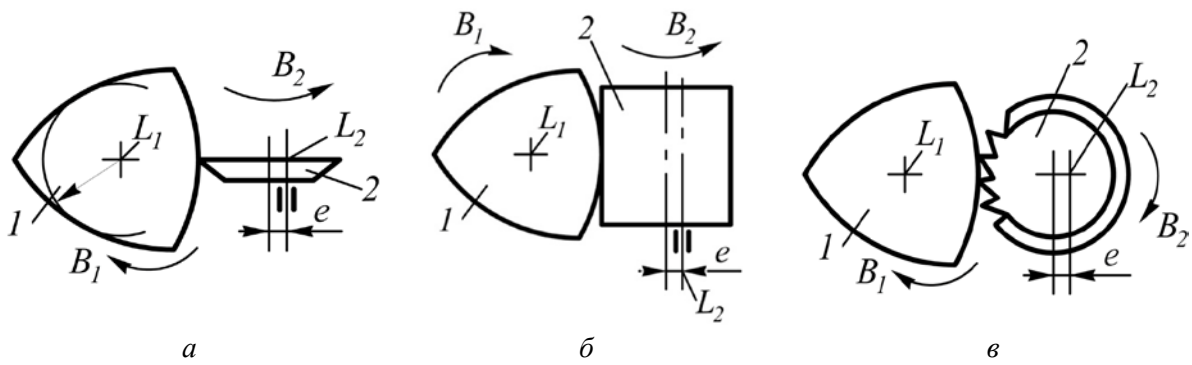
Схемы профилирования некруглых поверхностей эксцентрично установленными: круглым резцом *a*; цилиндрическим инструментом (фрезой, опилователем, шлифовальным кругом и др.) *б*; дисковой фрезой *в*.
